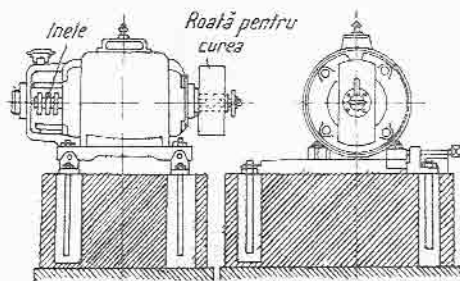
Motor asincron cu rotor bobinat și inele.
